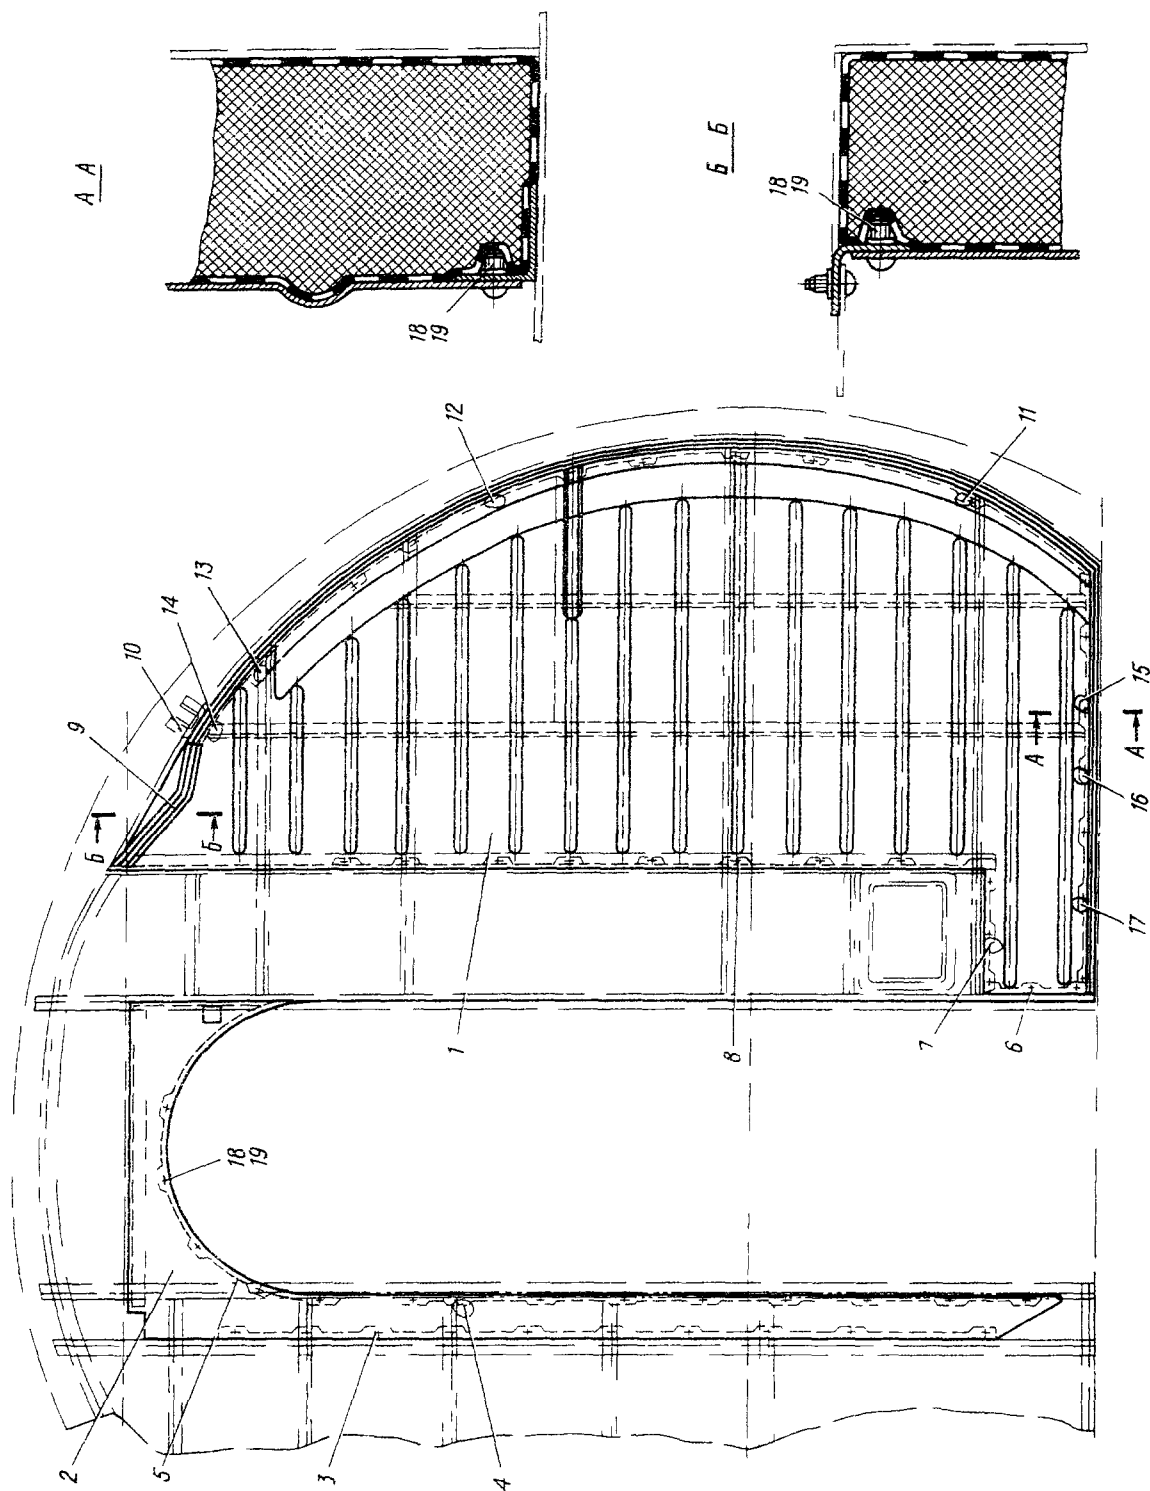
ОБЛИЦОВКА ШПАНГОУТА 7 СО СТОРОНЫ ГРУЗОВОЙ КАБИНЫ
